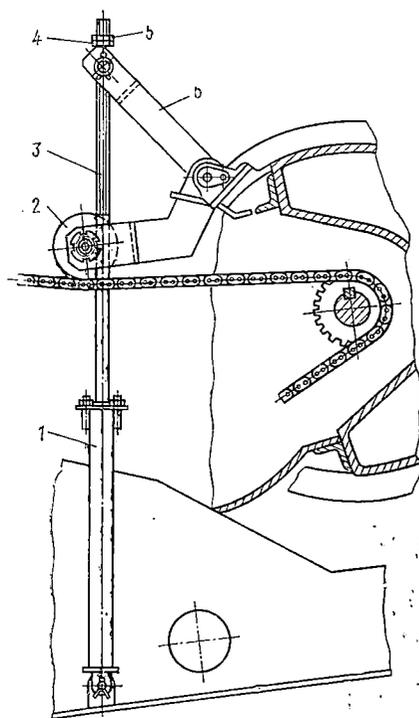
Натяжное устройство цепи экскаватора Э-652Б:
